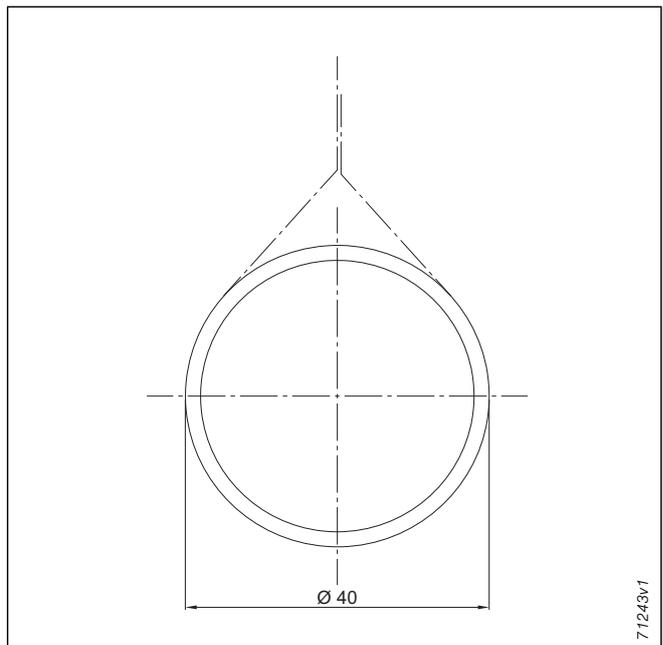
Fallprofil rund, groß, stoffumschlungen
